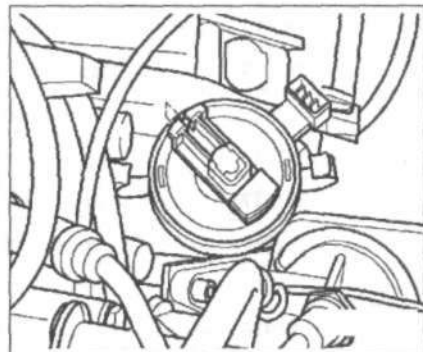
Вставьте распределитель так, чтобы метка ВМТ цилиндра №1 на роторе совместилась с меткой на корпусе распределителя.
